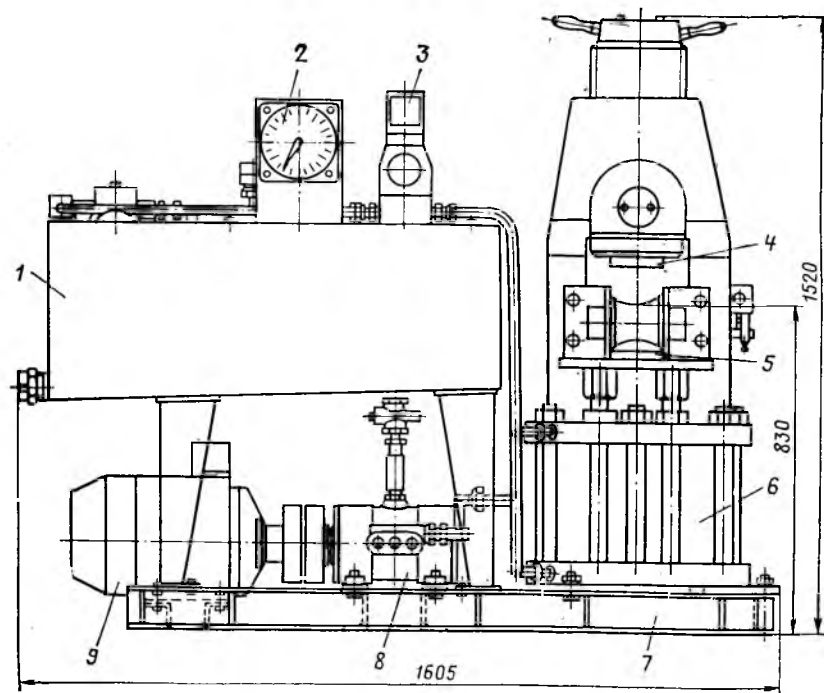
Станок для резки арматурной стали СМЖ-175А
